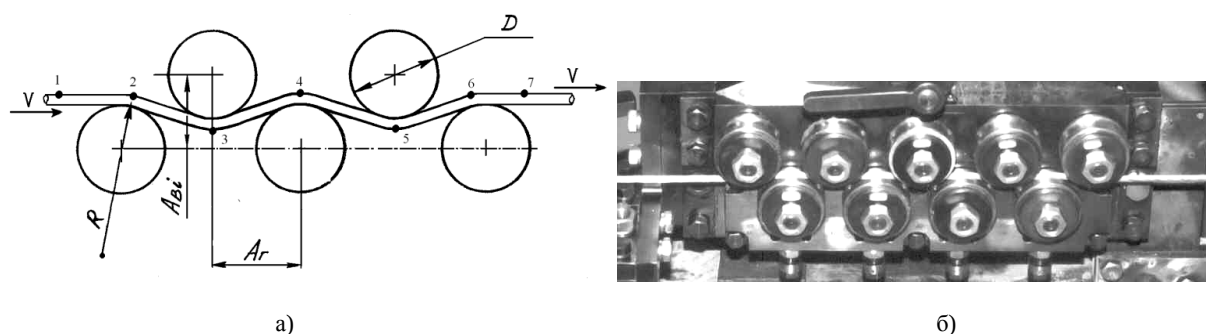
Кинематическая схема процесса (а) и внешний вид устройства для рихтовки длинномерного изделия (б)
